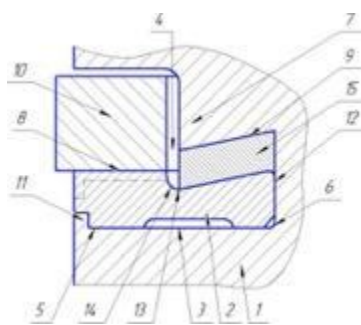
Схема установки противоизносного кольца с металлической проставкой: 1 – поршень; 2 – противоизносное кольцо; 3 – боковая поверхность кольца; 4 – поршневая канавка; 5 – нижняя горизонтальная опорная поверхность кольца; 6 – кольцевая проточка; 7 – внутренняя цилиндрическая стенка канавки; 8 – верхняя горизонтальная опорная поверхность противоизносного кольца; 9 – демпфирующий кольцевой лаз; 10 – поршневое кольцо; 11 – упорный выступ прямоугольного сечения; 12 – большая сторона трапеции цилиндрической стенки; 13 – меньшая сторона трапеции цилиндрической стенки; 14 – кольцевая проточка противоизносного кольца; 15 – металлическая проставка.
